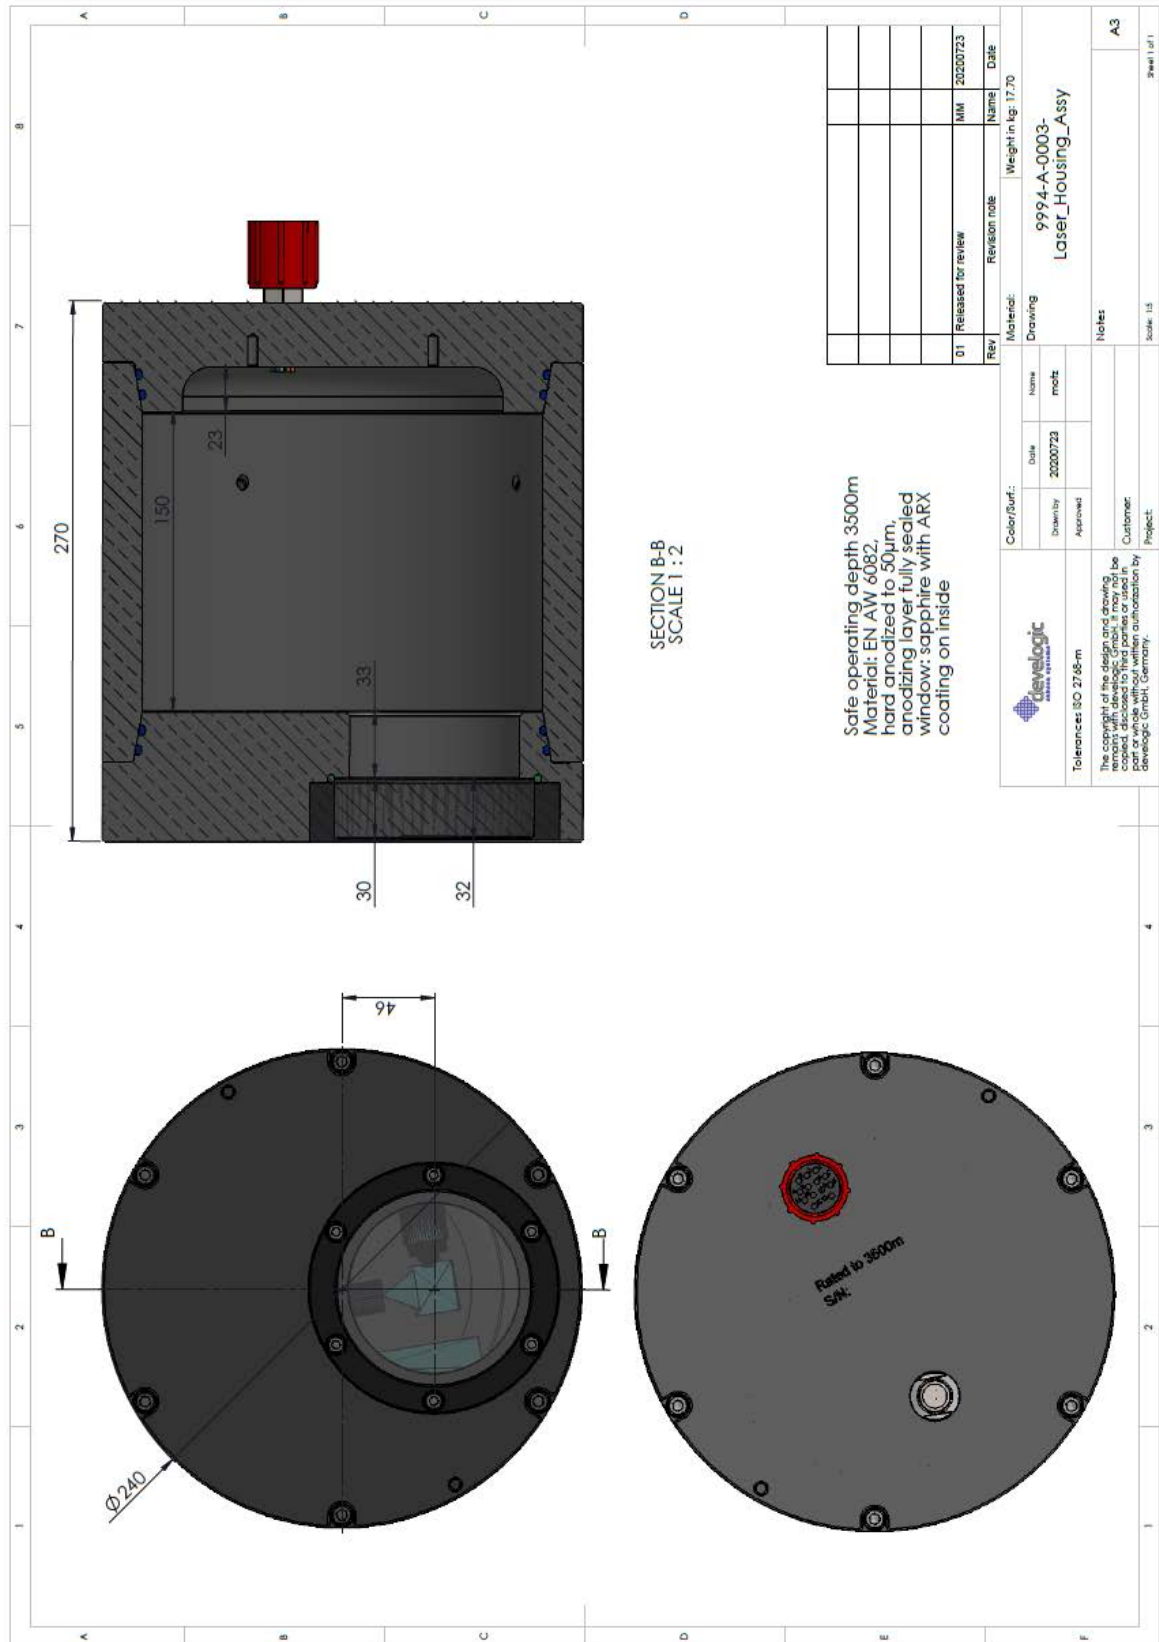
Desenho técnico de construção do encapsulamento de projeção de luz estruturada.
